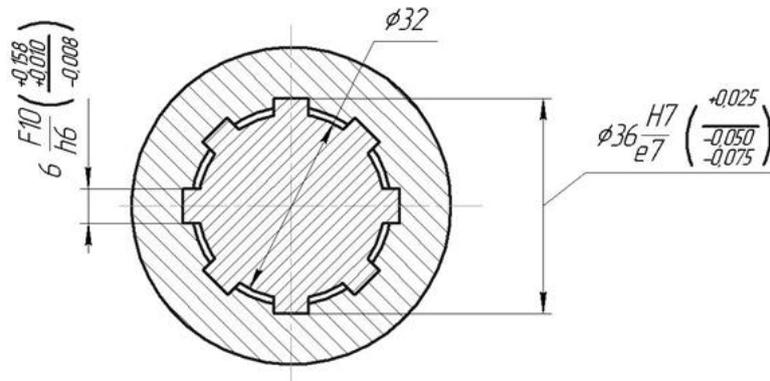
Ескіз деталей шліцевого з'єднання
